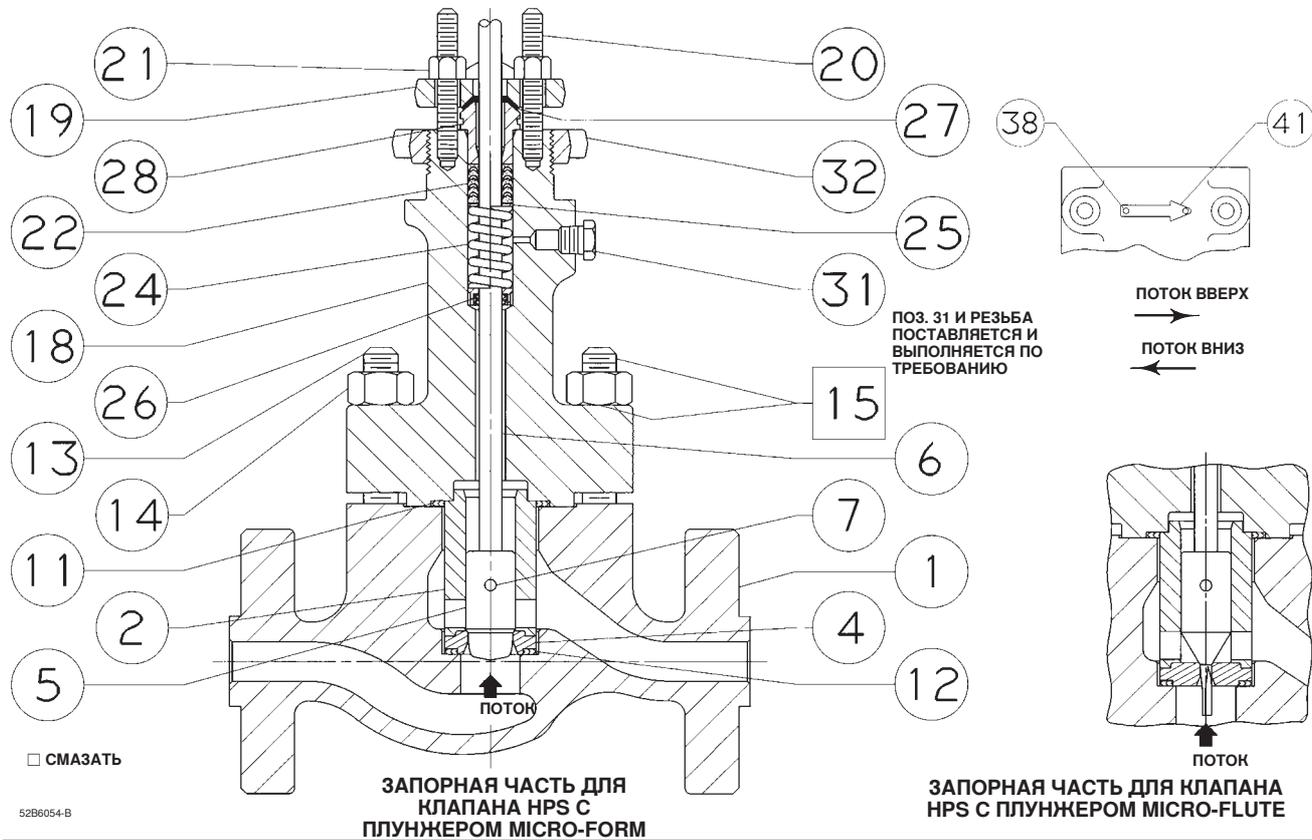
Клапан НРАД для номинального размера трубы 2 дюйма
